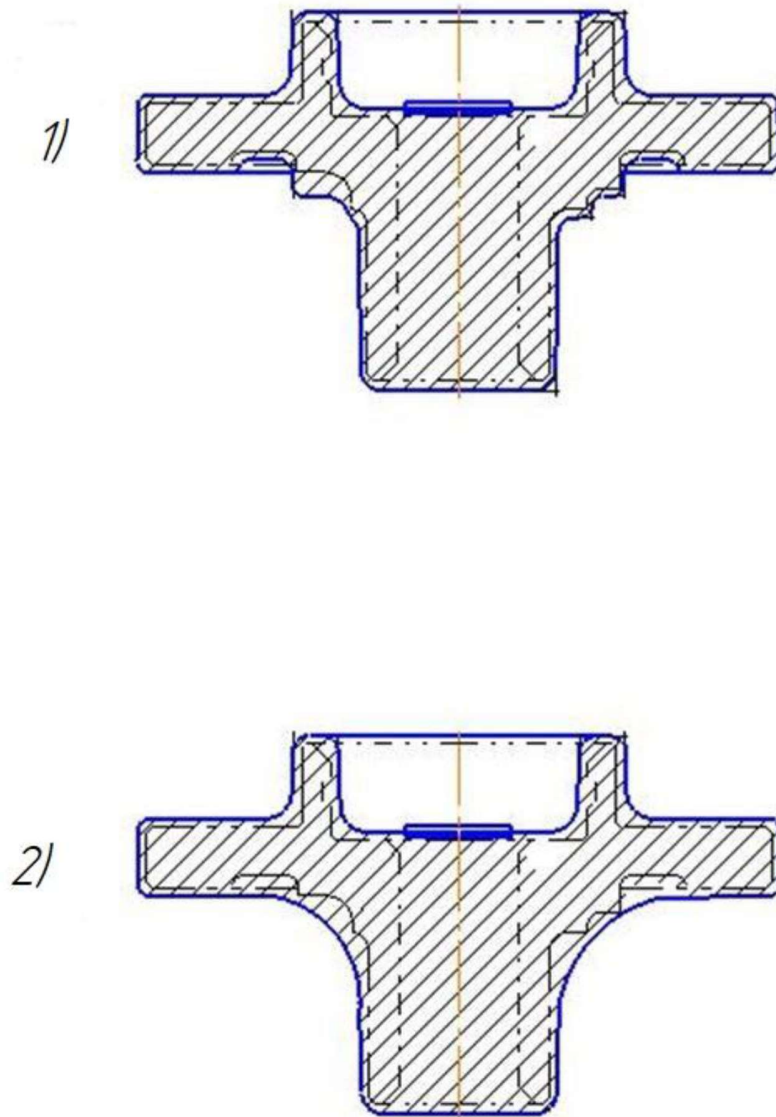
Заготовки: 1 – штампування 2 – лиття
